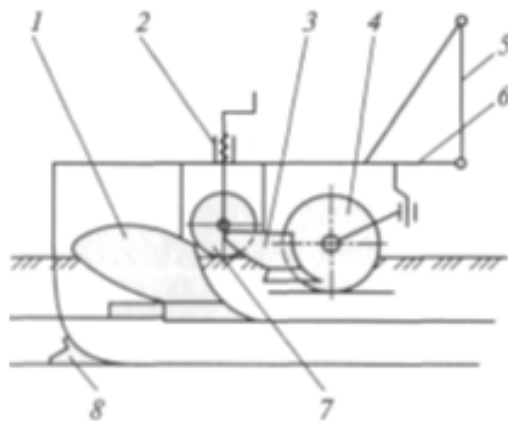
Загальна конструкція однокорпусного начіпного плуга: 1 — корпус плуга; 2 — гвинтовий механізм опорного колеса; 3 — передплужник; 4 — ніж; 5 — начіпний пристрій; 6 — рама; 7 — опорне колесо; 8 — ґрунтопоглиблювач
